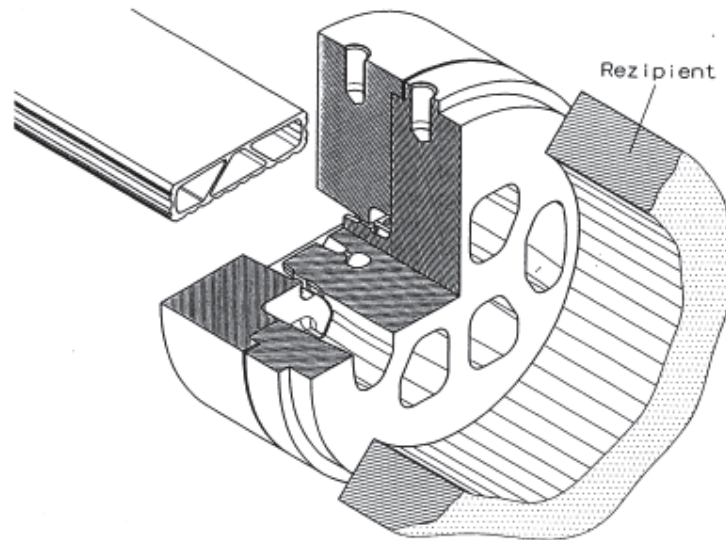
Kammerwerkzeug bzw. Hohlwerkzeug
